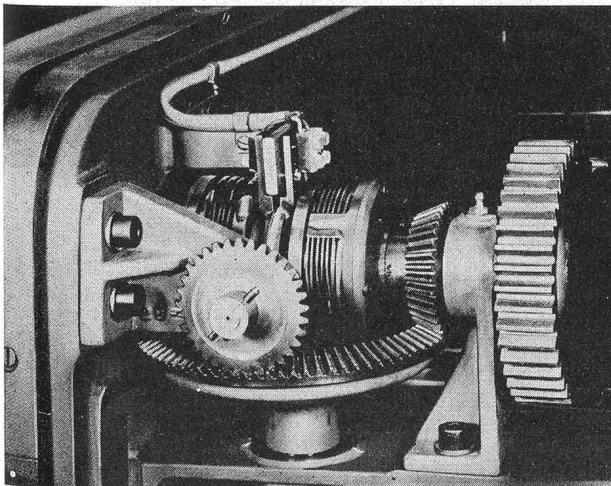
Elektromechanisches Wendegetriebe (Teilansicht)
